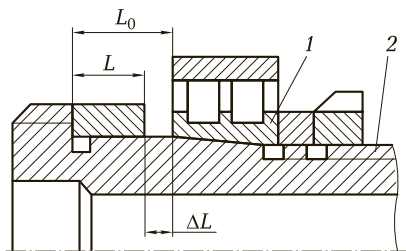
Схема регулирования предварительного натяга в узлах с роликовыми двухрядными подшипниками с цилиндрическими роликами:
